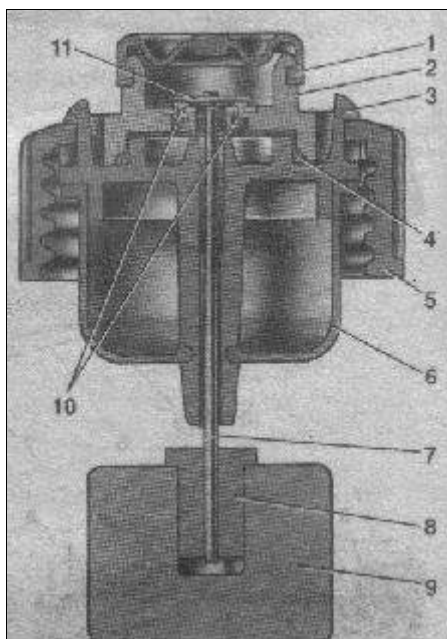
Датчик аварійного рівня гальмової рідини: 1 – захисний ковпачок; 2 – корпус датчика; 3 – підстава датчика; 4 – ущільнювальне кільце; 5 – затискне кільце; 6 – відбивач; 7 – штовхач; 8 – втулка; 9 – поплавець; 10 – нерухливі контакти; 11 – рухливий контакт.
